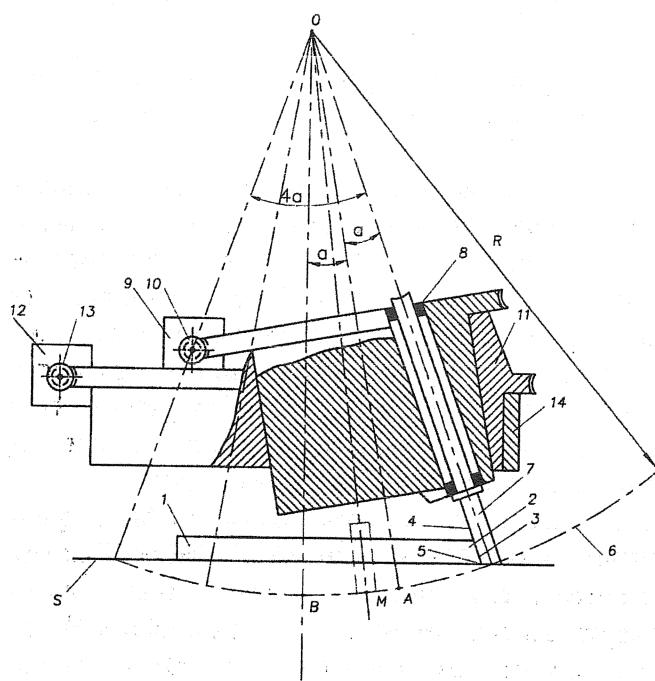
Фрезерная головка для двухкоординатной обработки конической поверхности
